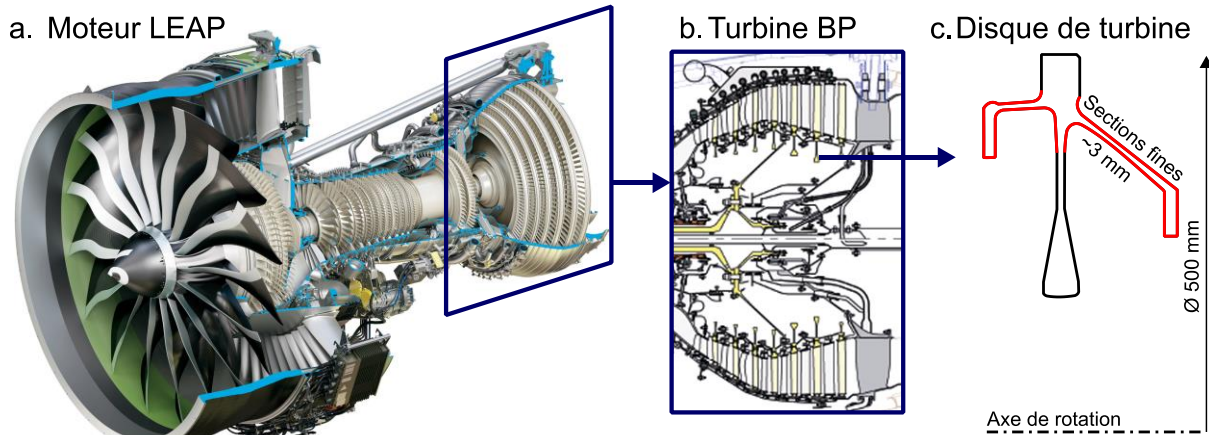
a - Moteur LEAP, b - Vue en coupe de la turbine Basse Pression (BP), c - Vue en coupe d'un étage de disque de la turbine BP, brides surlignées en rouge (Source SAFRAN).
